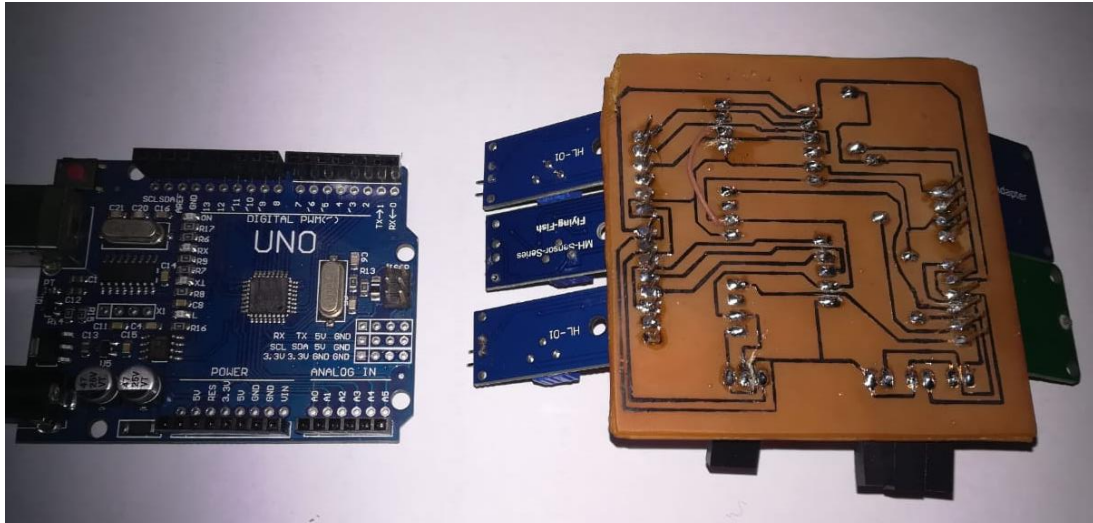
PCB y componentes eléctricos soldados para el modulo del sistema de riego.
